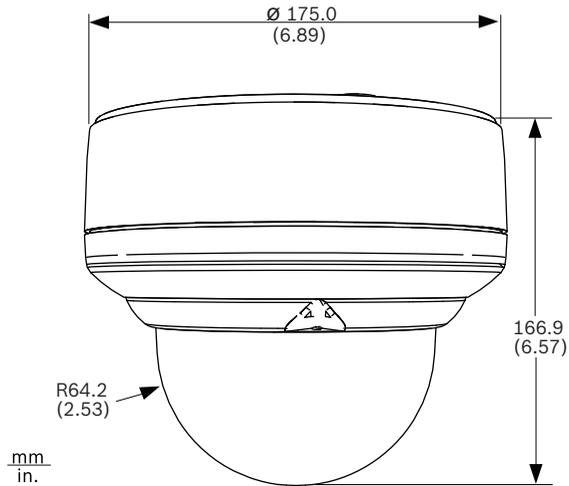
Dimensions du support de montage en surface pour l'intérieur
